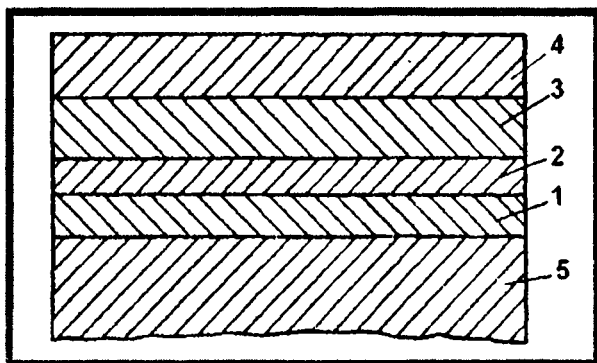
Схема многослойного покрытия для деталей из алюминиевых сплавов: 1 - адгезионный слой; 2 -промежуточный слой; 3 - рабочий слой; 4 - внешний слой из углеродной алмазоподобной пленки; 5 - основа
